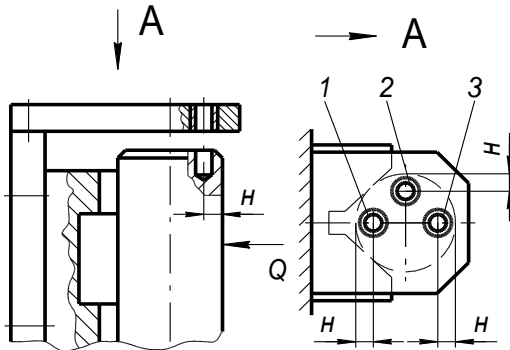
Варіанти схем розташування кондукторної втулки при свердлуванні отвору в торці вала (до задачі 8).
